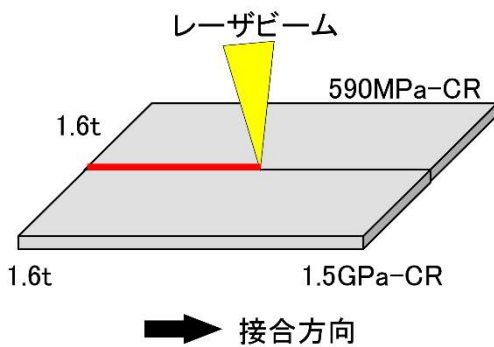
レーザ溶接の概略図
